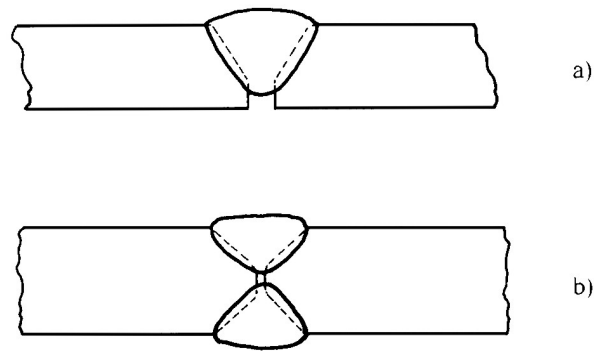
Diferentes tipos de falta de penetração a) penetração incompleta na raiz, b) no interior da junta soldada.
